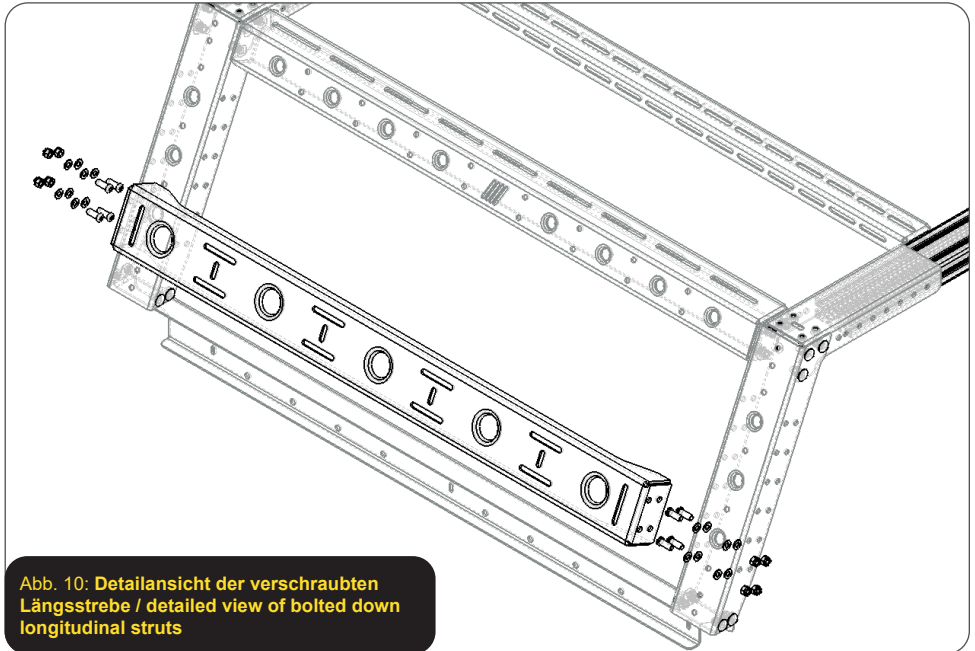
Detailansicht der verschraubten Längsstrebe / detailed view of bolted down longitudinal struts
